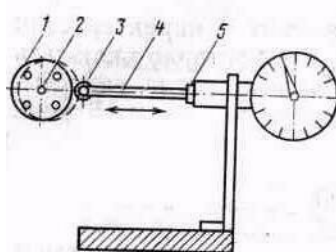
Прибор для проверки биений вала электродвигателя КПТ:
